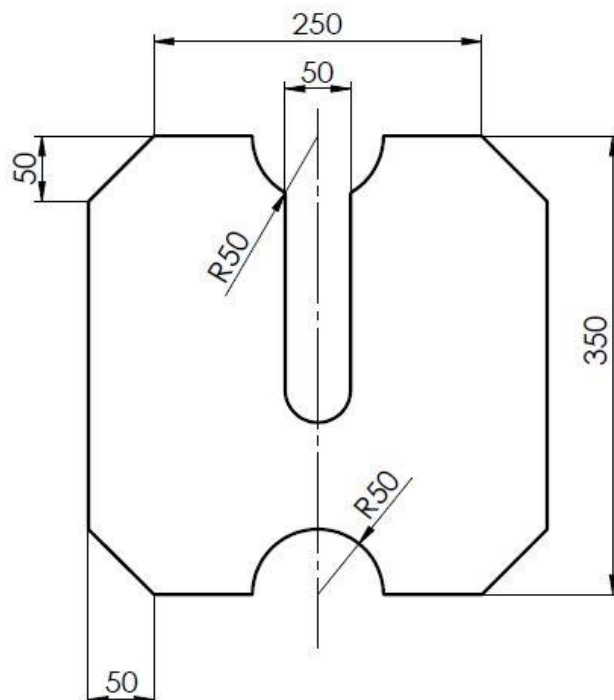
Esquema de placa de abertura horizontal do piloto.
